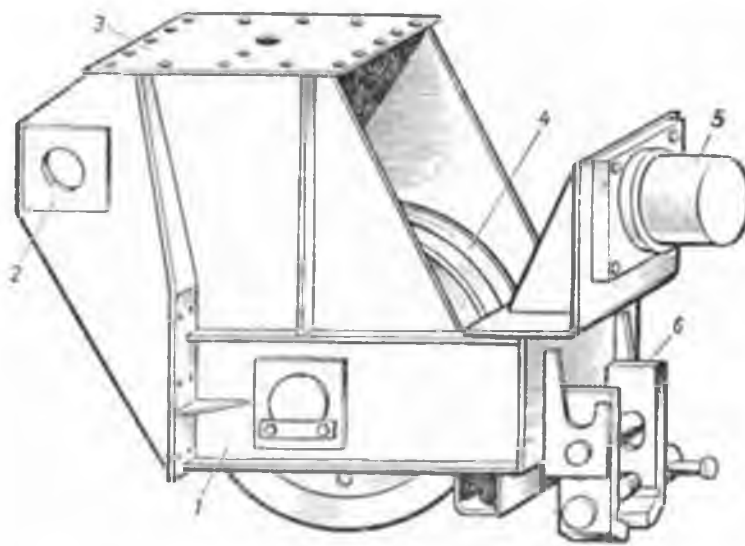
Холостий візок крана КК-5: 1-корпус; 2-цапфа балансира; 3 - опорний фланець стійки; 4- каток; 5 - буфер; 6 - рейкове захоплення
